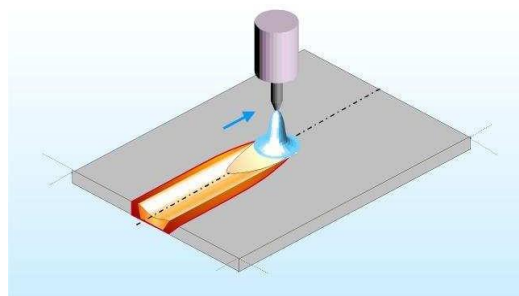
assemblage de 2 pièces par un métal (soudage) [45]
